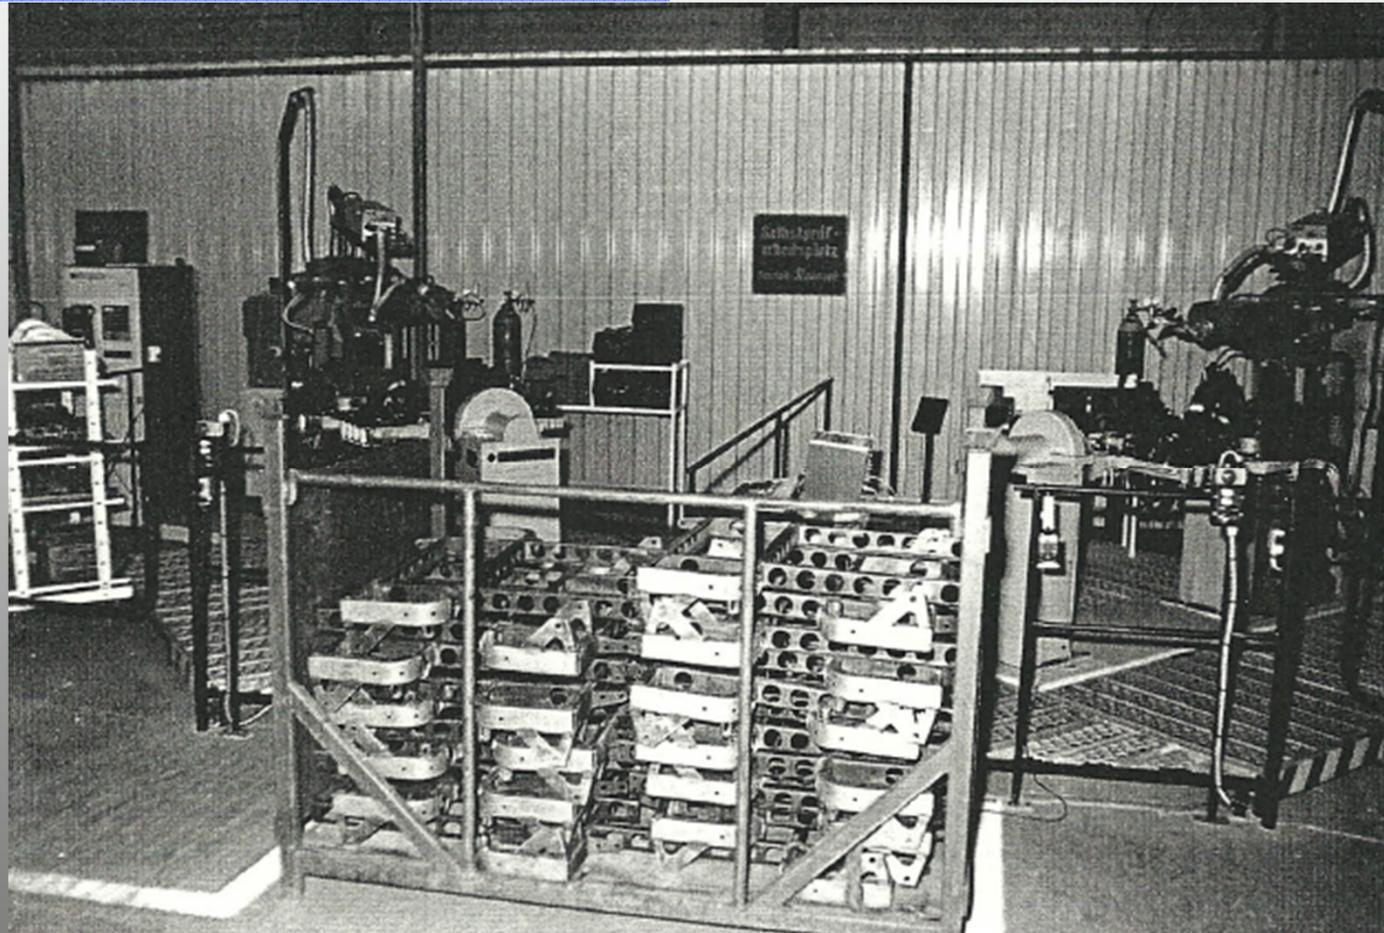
Arbeitsplatz gesamt mit 2 Schweißrobotern
